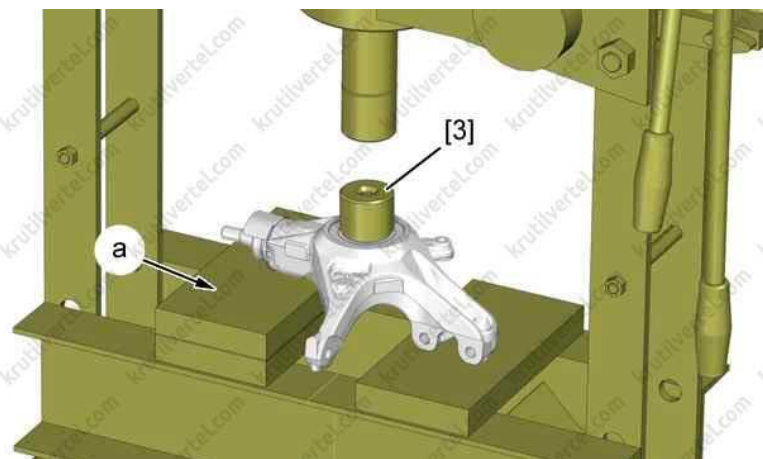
Випресування підшипника з поворотної цапфи
